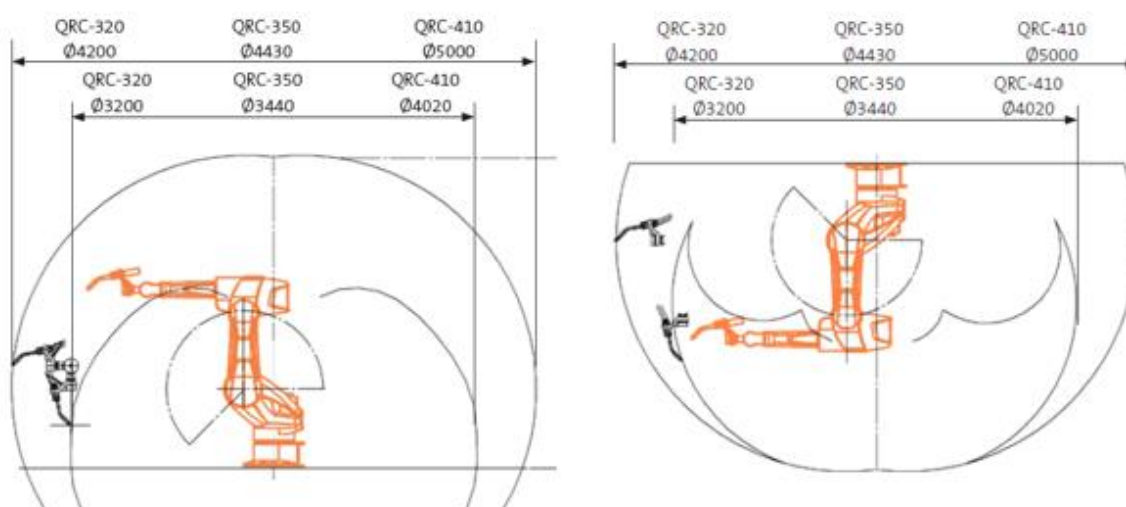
Volume di lavoro per un robot CLOOS QIROX QRC con installazione a pavimento (sx) e sopra-testa (dx)
